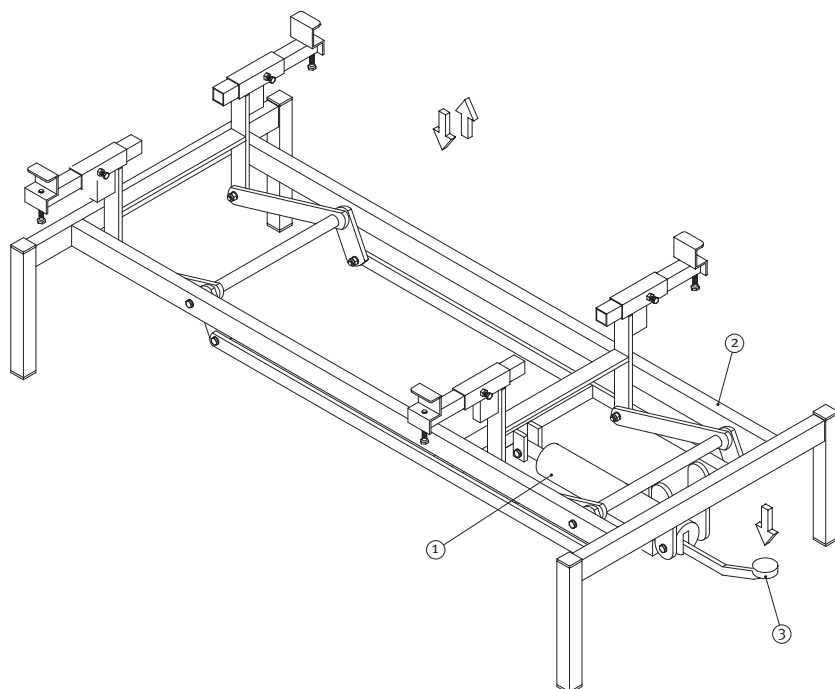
Regolazione verticale del piano rete del letto Art. A 7032/AO.
